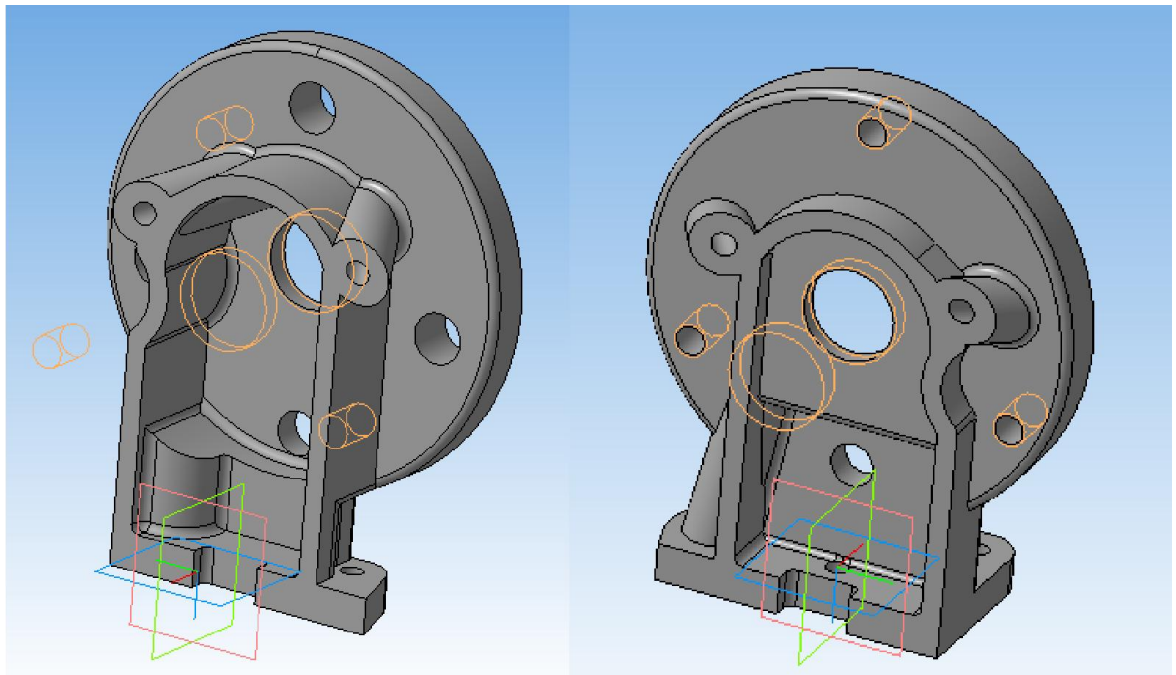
3D модель «Корпус переходника» с вырезом 1/2 части
